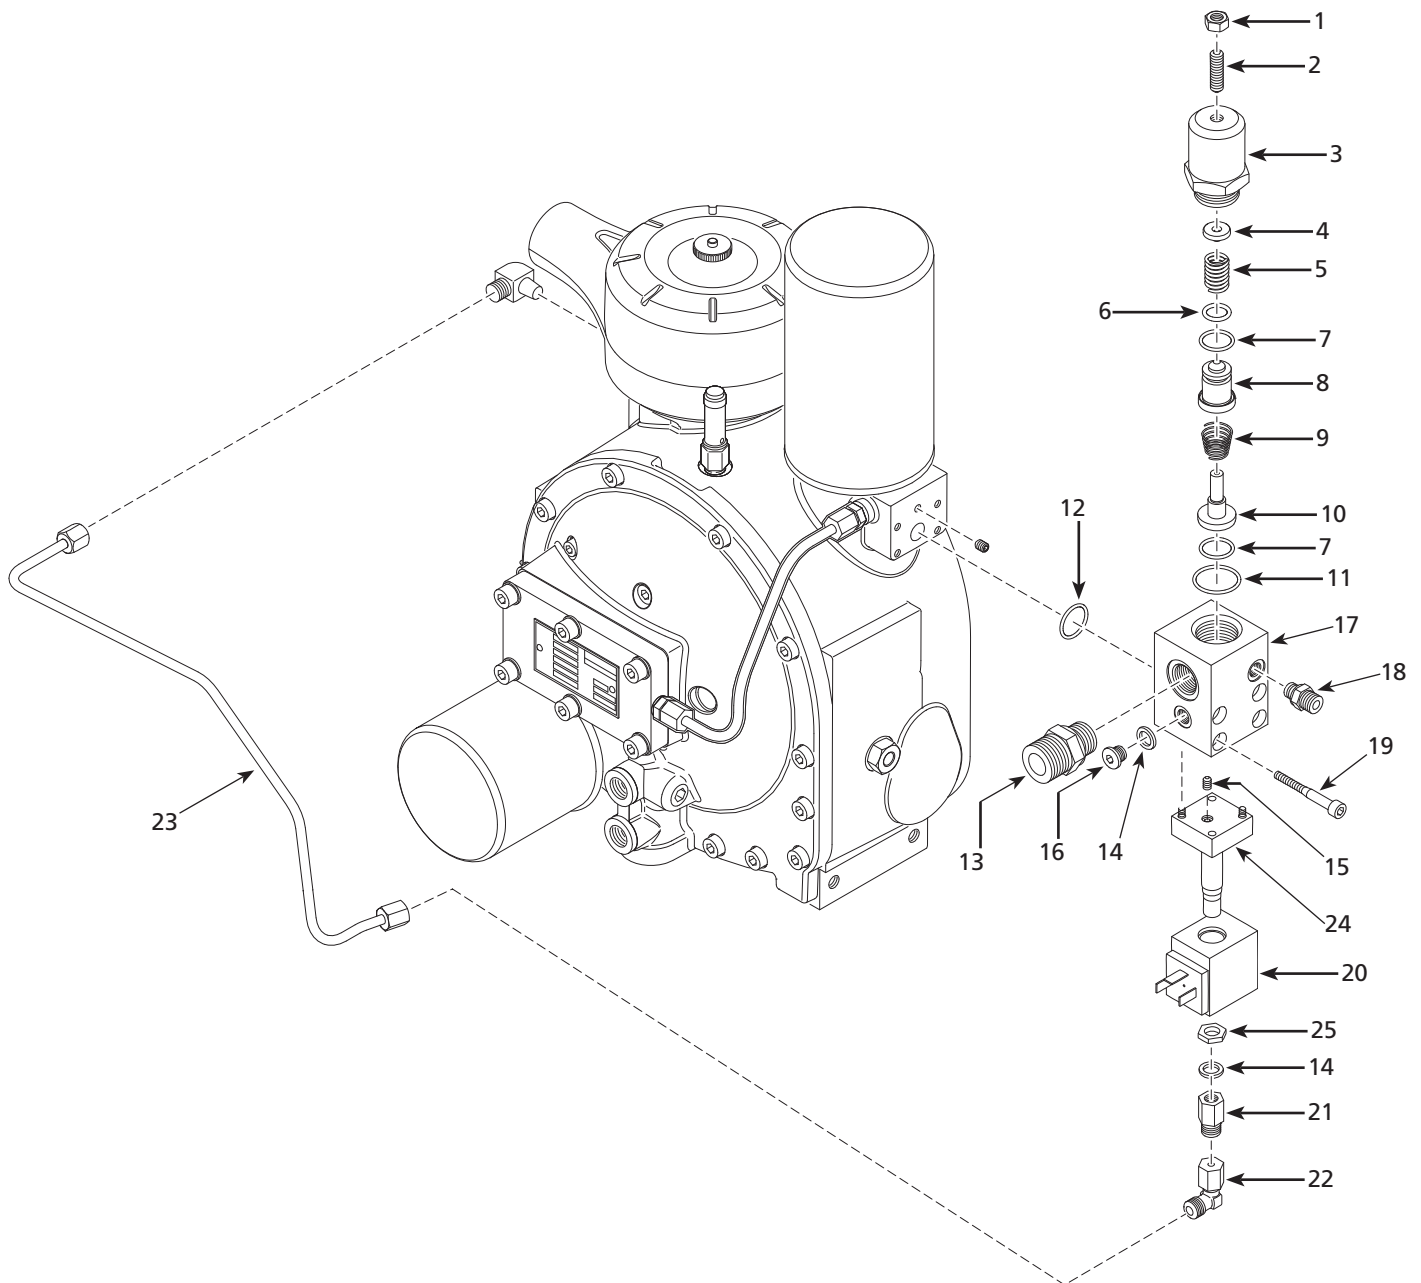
Illustration de pièces de réparation pour l'assemblage du collecteur de la vis rotative de 5 à 10 HP
